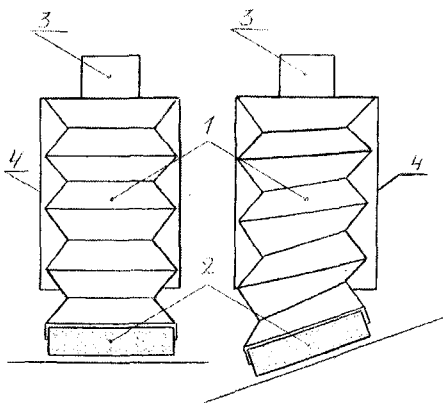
Использование сильфона для обработки плоскостей расположенных под разными углами: 1 – сильфон; 2 – наконечник; 3 – абразивный круг; 4 – направляющий цилиндр. Вид а - обработка перпендикулярной поверхности; вид б - обработка поверхности под углом меньше, больше 90 град.
